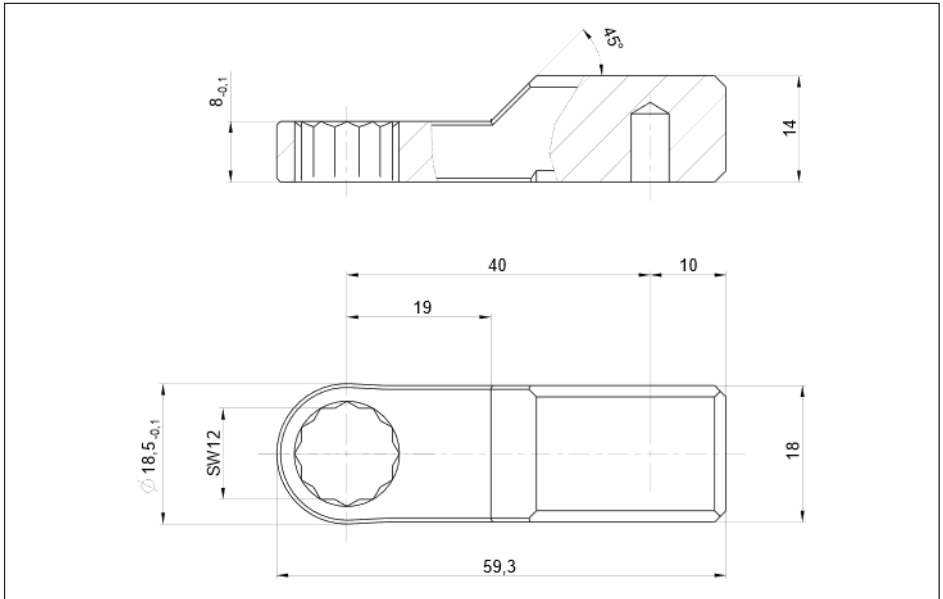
Ring-Einsteckwerkzeug SW12
